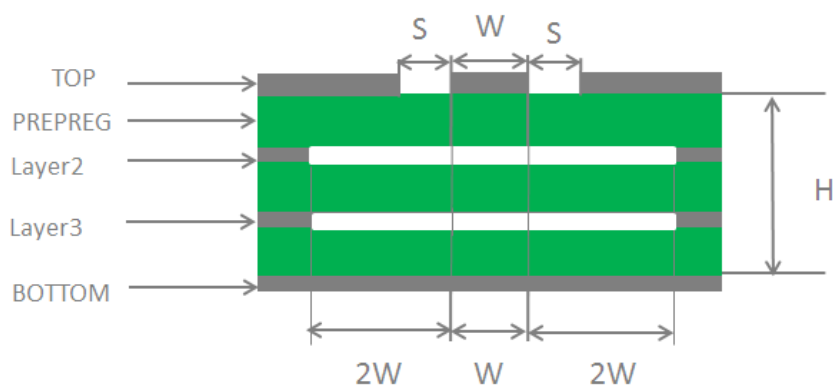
四层 PCB 板共面波导结构 (参考地为第四层)
